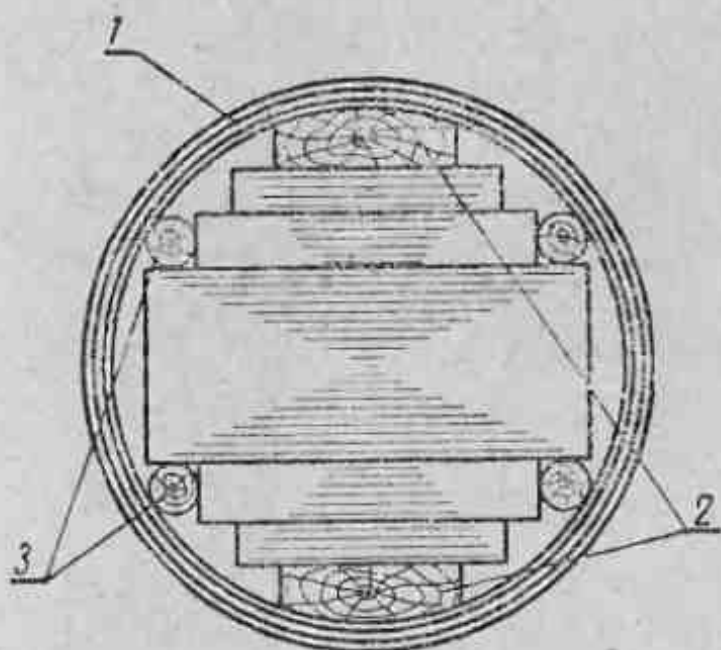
Прессовка стальных листов стержней деревянными планками:
